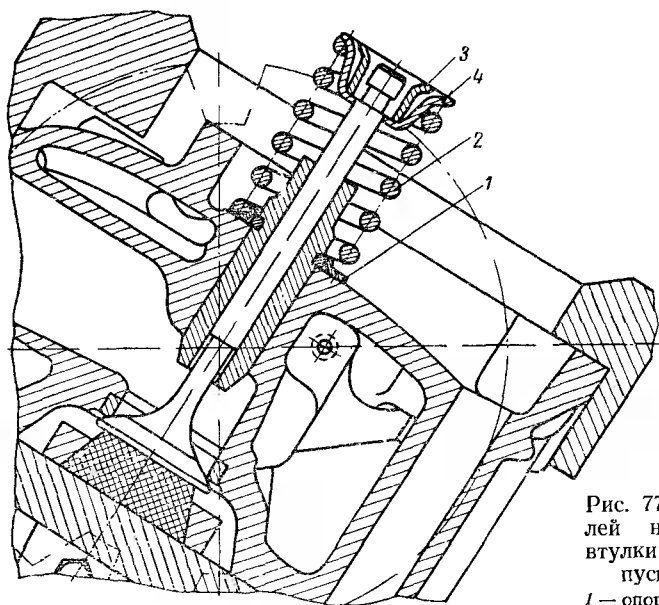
Установка деталей на направляющие втулки и стержень выпускного клапана:
